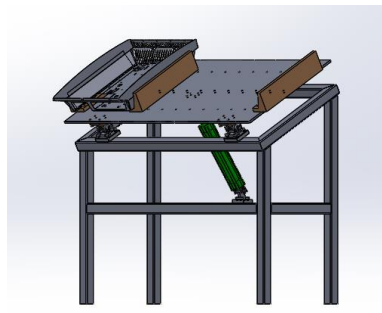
Assemblage de l'adaptateur du poste de soudage capot
